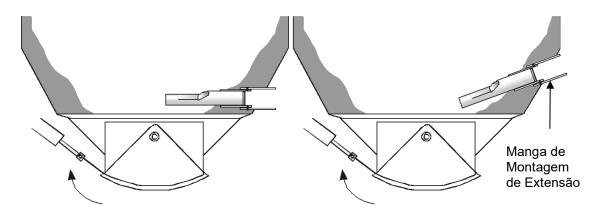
Montagem do Hydro-Probe nos Depósitos Grandes
